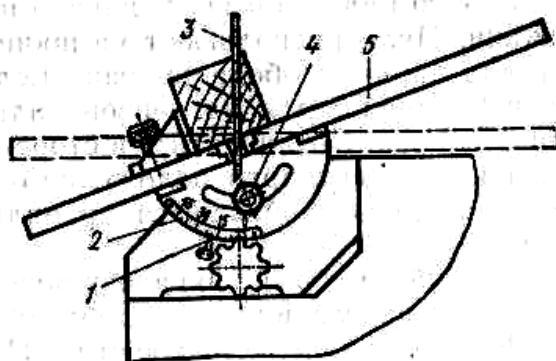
Настройка стола ленточнопильного столярного станка: 1 — указатель, 2 — шкала, 3 — пила, 4 — гайка, 5 — стол
